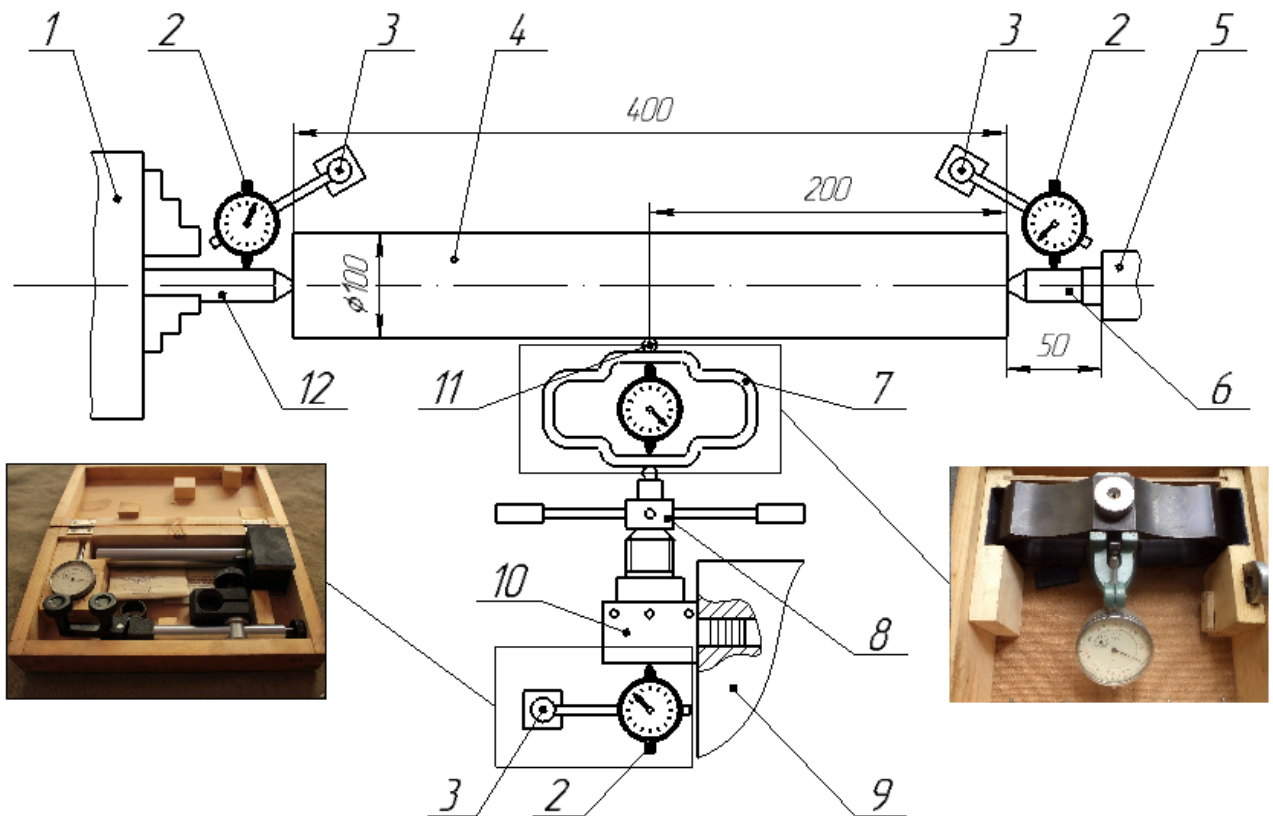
Схема установки для измерения жёсткости токарного станка методом статического нагружения: 1–передняя бабка с патроном; 2– Индикатор 1 МИГ-1 ГОСТ 9696-82; 3–магнитная стойка для индикатора; 4–центровая оправка; 5–корпус задней бабки; 6, 12–задний и передний центр; 7–динамометр ДОУМ-3-100 И ГОСТ 9500-84; 8–поджимной винт; 9 - револьверная головка; 10– инструментальный блок; 11 -шарики стальные закаленные.
